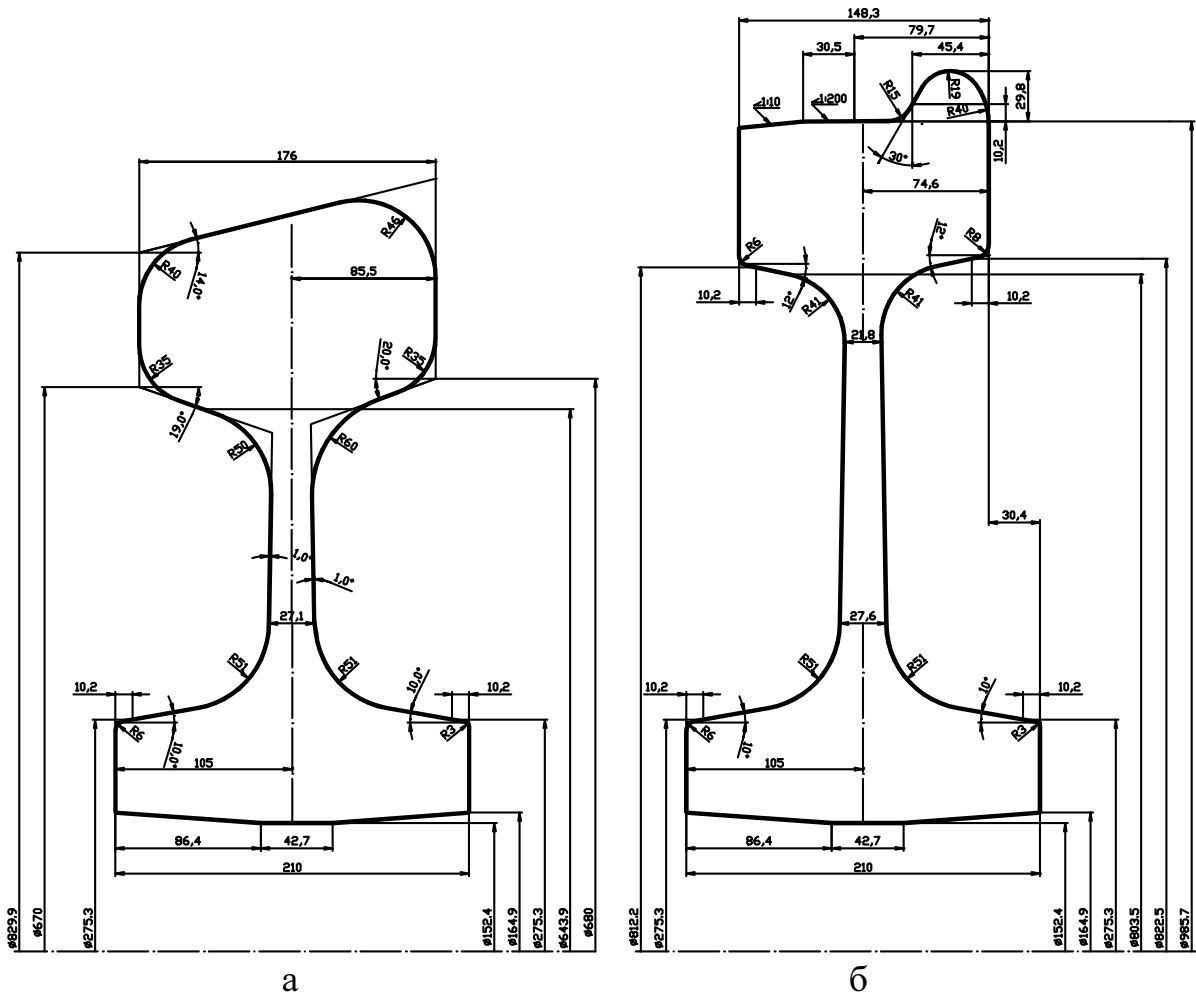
Колесная заготовка (а) и прокатываемое из него черновое колесо (б) (существующая калибровка по металлу)
